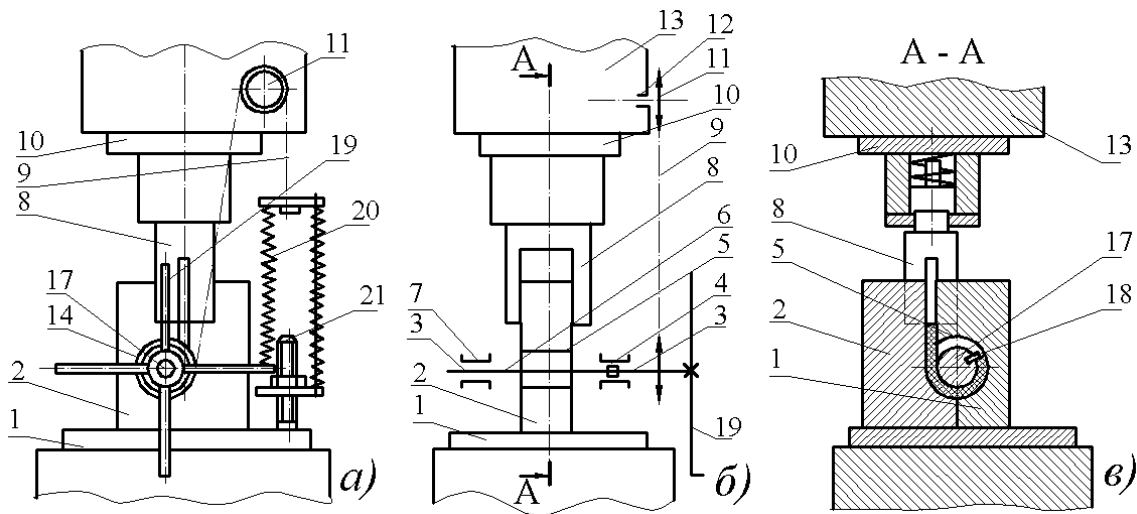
Схематичне зображення пристрою для виготовлення втулок із листових заготовок
